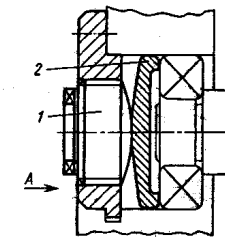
Способ крепления и регулировки радиально-упорного подшипника
